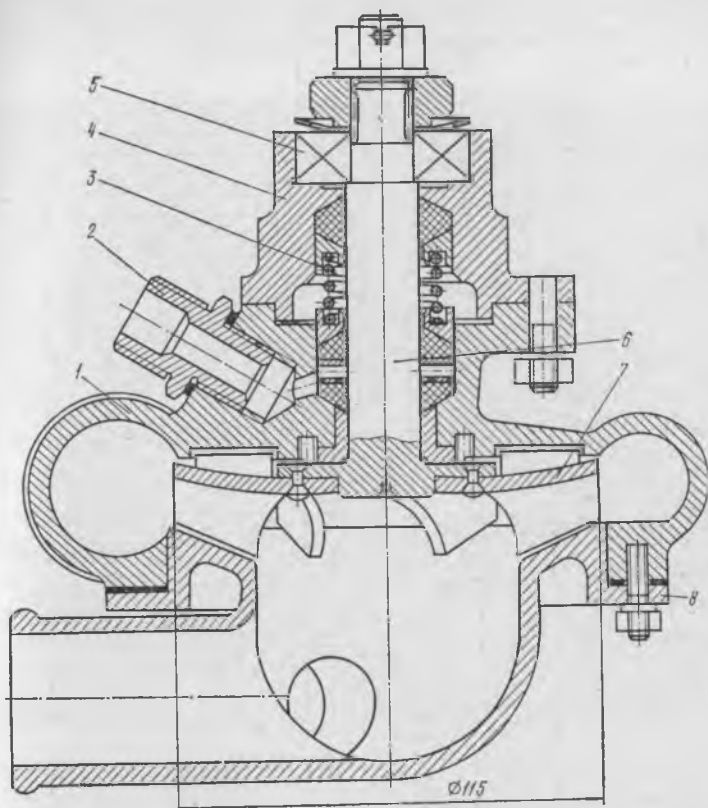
Циркуляционный центробежный одноступенчатый насос с вертикальным расположением вала:
